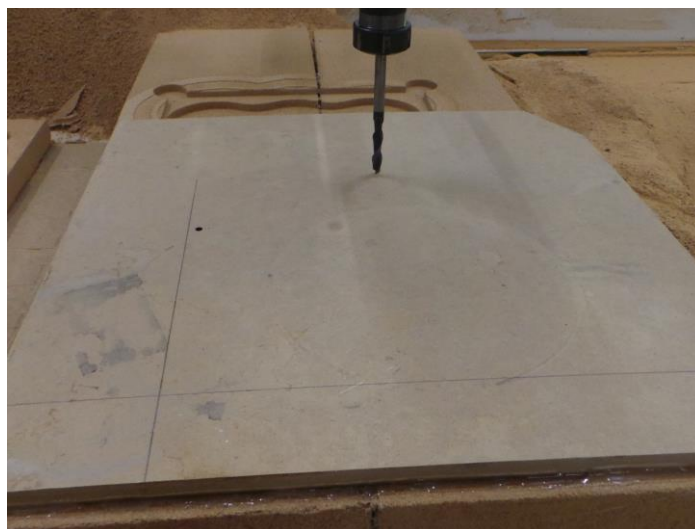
Ponta da ferramenta no terceiro ponto necessário para definir um plano.
